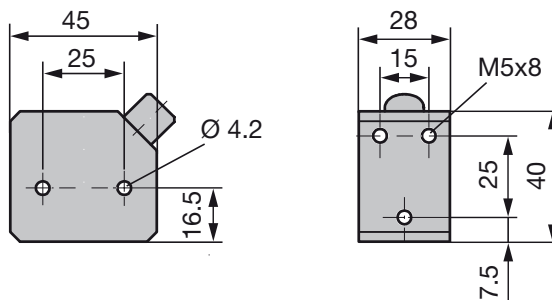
Medidas de montaje del sensor de posición BTL5-P-4500-1
